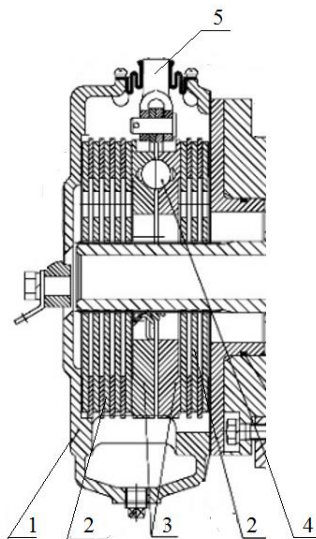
ТМ базовой конструкции: 1 – корпус; 2 – пакет дисков; 3 – нажимные диски; 4 – шариковый механизм сжатия дисков
